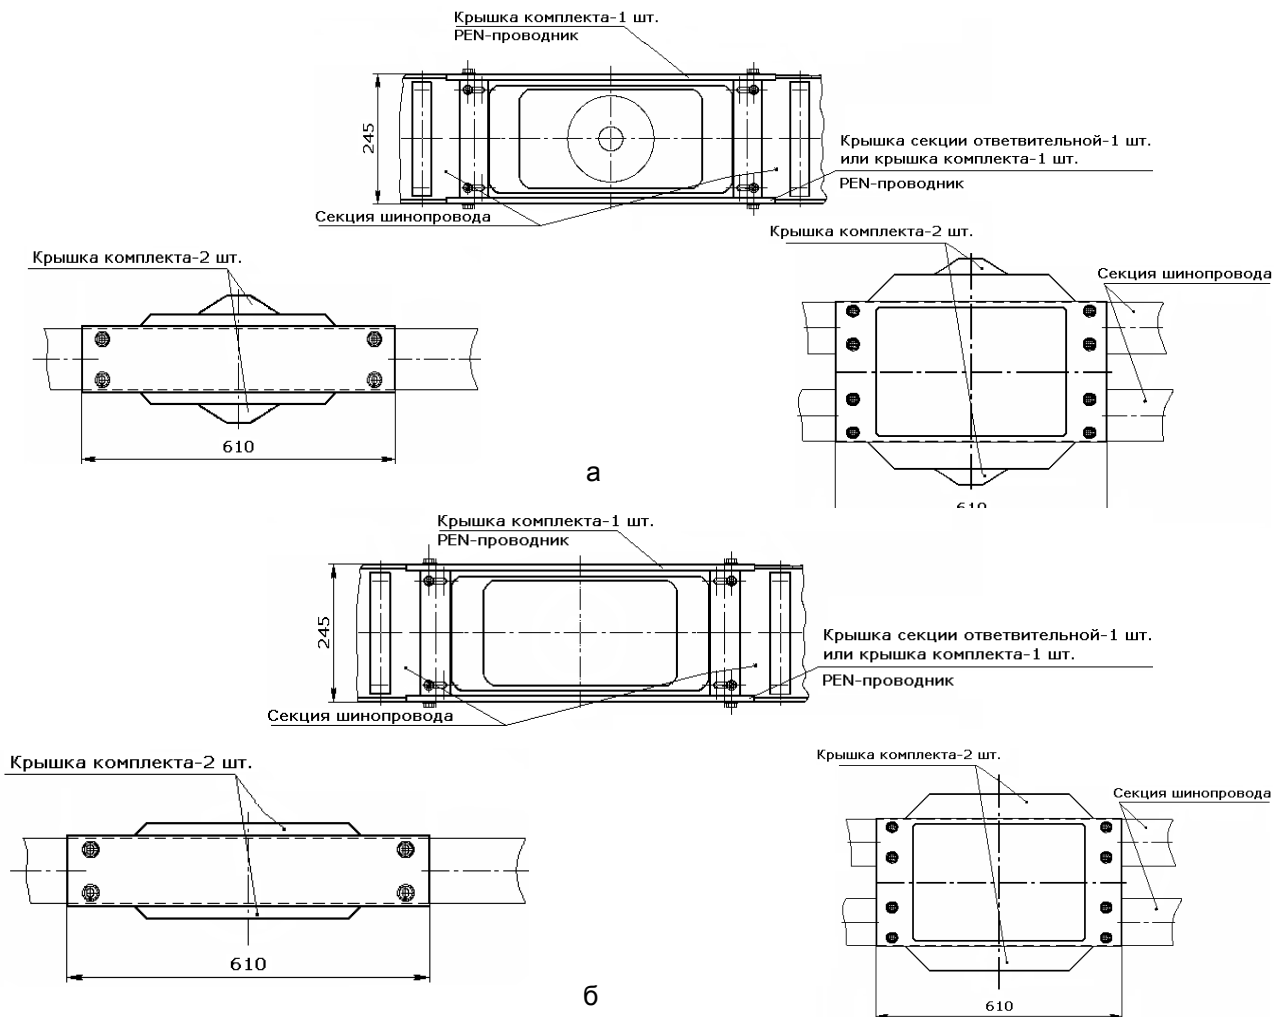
Стыковочные комплекты на токи 1250А, 1600А, 2500А и 3200А.
